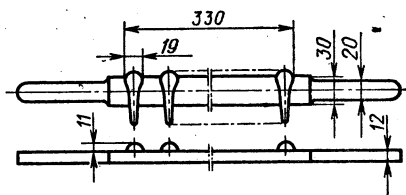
Деревянный штамп для формирования корпусов конфет «Шоколадные бутылочки»
